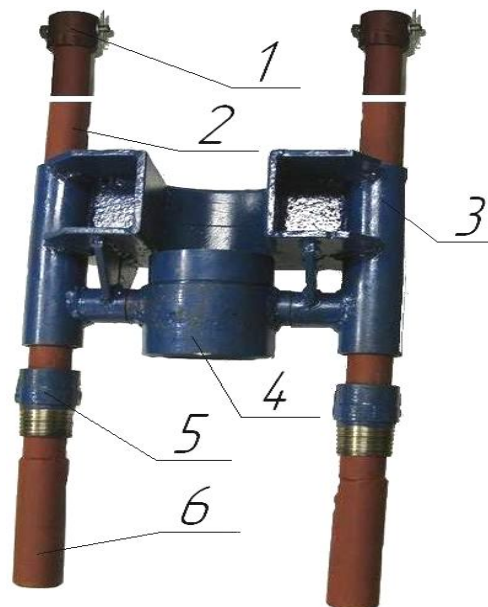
Направляющий узел в сборе: 1 - съемный ограничитель; 2 - направляющая стойка 3 - направляющая каретка; 4 - поворотная воронка; 5 - монтажная втулка; 6 - опорный патрубок.
